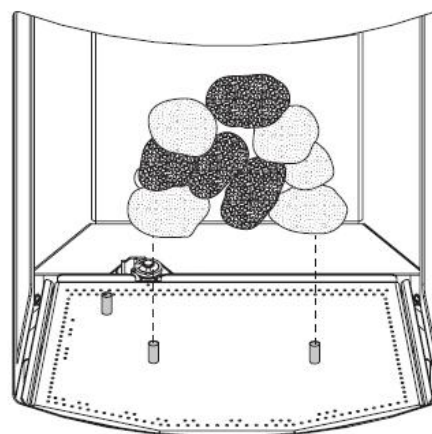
Installation du tas de pierres, au milieu du lit de pierres (option «Wishing Rocks»)
